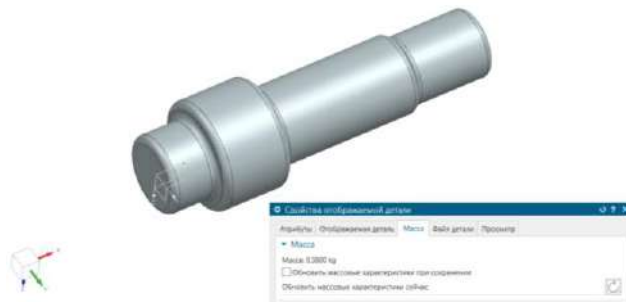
3D-модель заготовки, отриманої на КГШП
